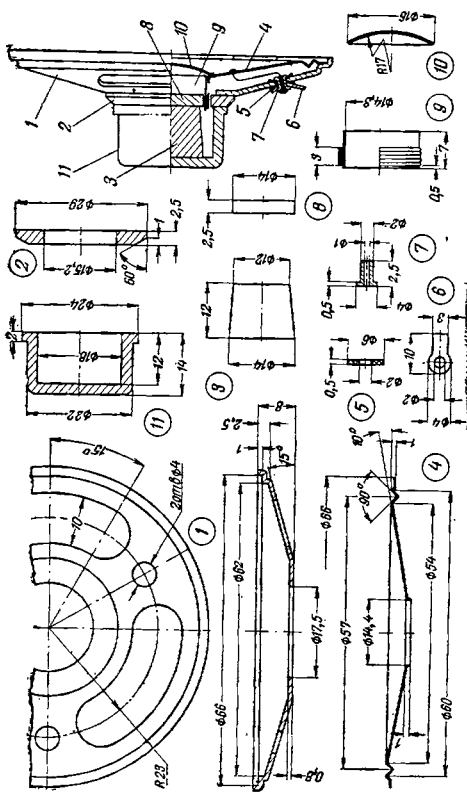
Конструкция громкоговорителя и размеры его деталей.
